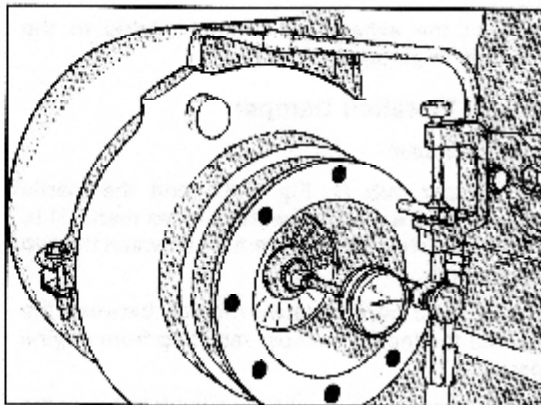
(OM1065L). Проверка подшипника и зазора турбонаддува.
